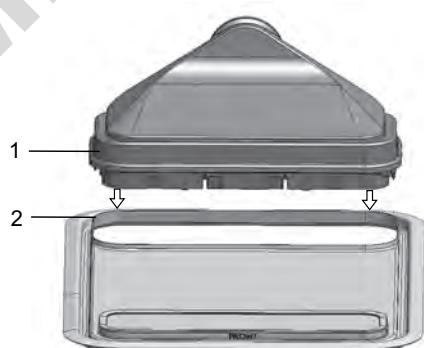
Monter le boîtier du filtre à air sur le couvercle du réservoir d'eau
